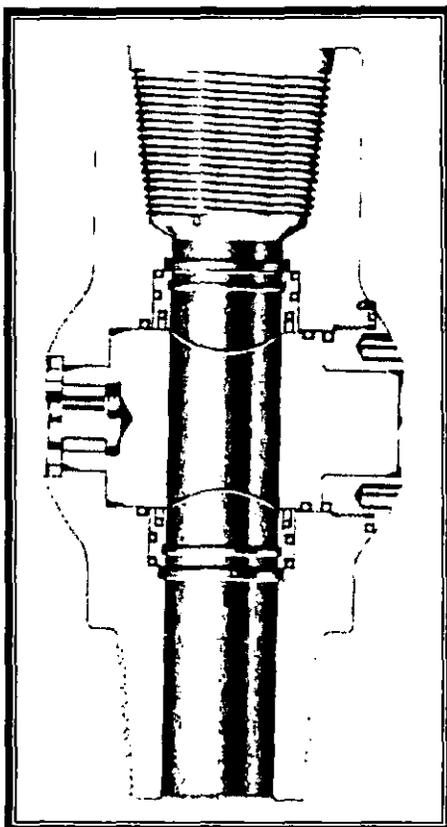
Válvula macho para flecha.<sup>1</sup>
